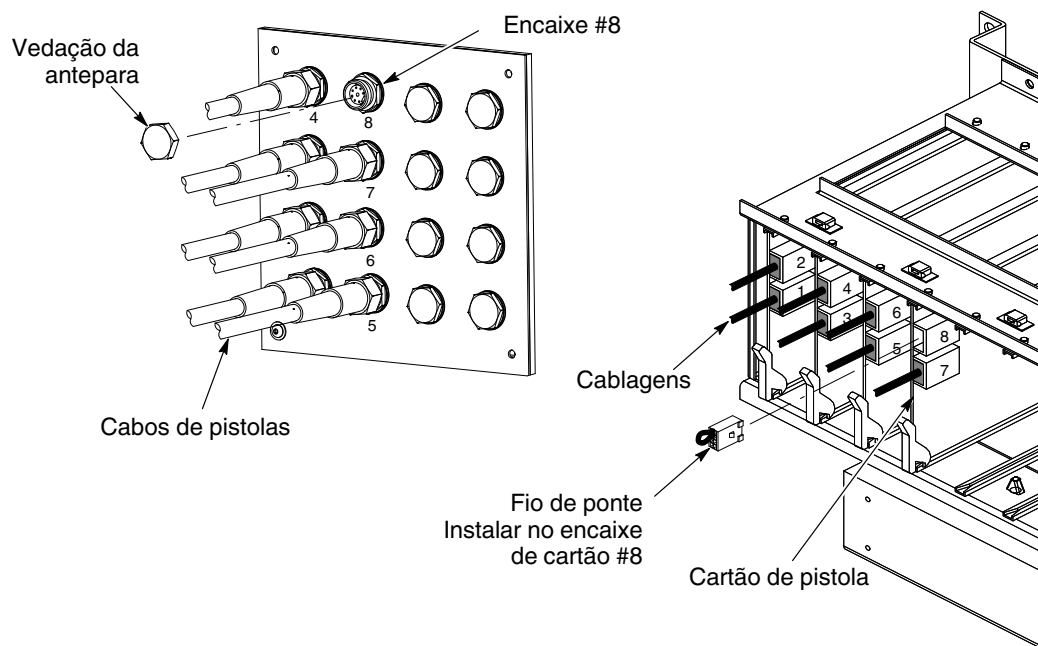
Instalação de vedações e fios de ponte - Exemplo mostrando um sistema de 8 pistolas com 7 pistolas
